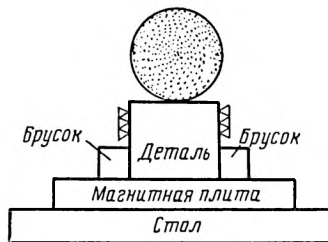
Схема установки изделия для шлифования плоскостей под углом 90°
